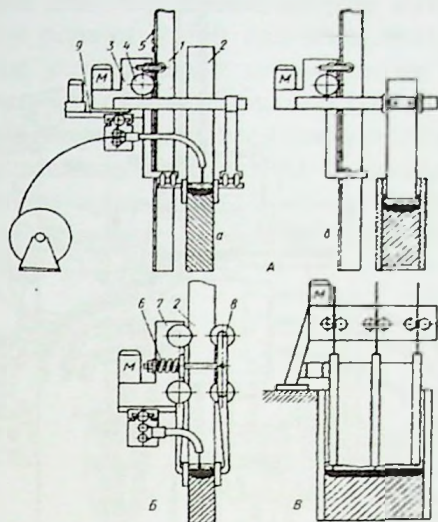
Аппараты для электрошлаковой сварки:
